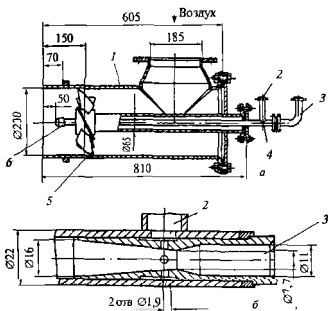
Горелка для сжигания природного газа при распыливании в факеле воды. а — общий вид, б — газовойодяной смеситель, 1 — воздухоподводящий корпус; 2 — подвод воды; 3 — подвод газа; 4 — смеситель; 5 — завихритель; 6 — выходное сопло
